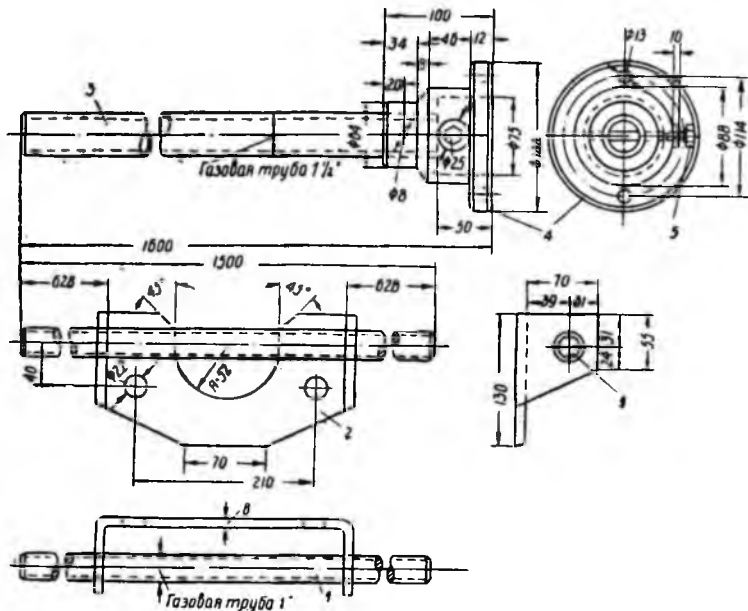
Приспособление для снятия и постановки коленчатого вала ЧТЗ-С-60:
